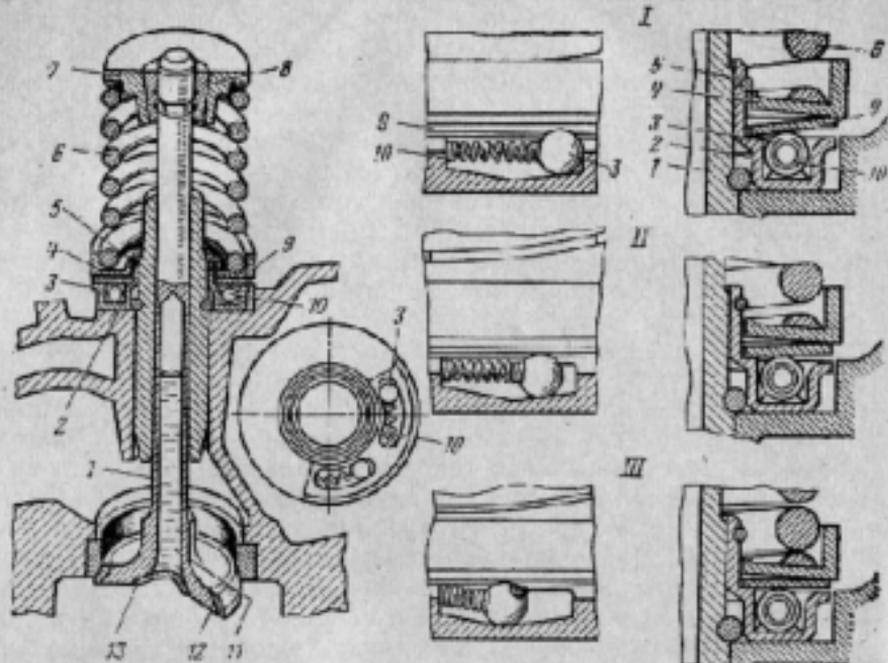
Выпускной клапан в сборе с механизмом вращения и схема его работы: 1 — выпускной клапан; 2 — неподвижный корпус механизма вращения; 3 — шарик механизма вращения; 4 — упорная шайба; 5 — замочное кольцо; 6 — пружина клапана; 7 — тарелка пружины клапана; 8 — сухари клапана; 9 — дисковый втулка механизма вращения; 10 — возвратная пружина механизма вращения; 11 — латисное направление клапана; 12 — жикерочная шайба рабочей фаски клапана; 13 — заглушка клапана; I — начальное положение механизма вращения; II — рабочее положение; III — конечное положение
